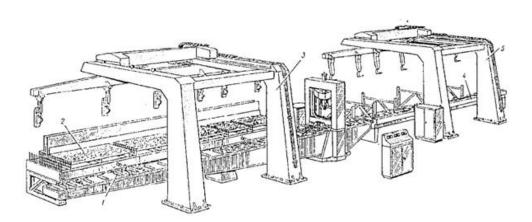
Схема поточной линии механизированного изготовления прямых тавровых балок МИБ-700A.
